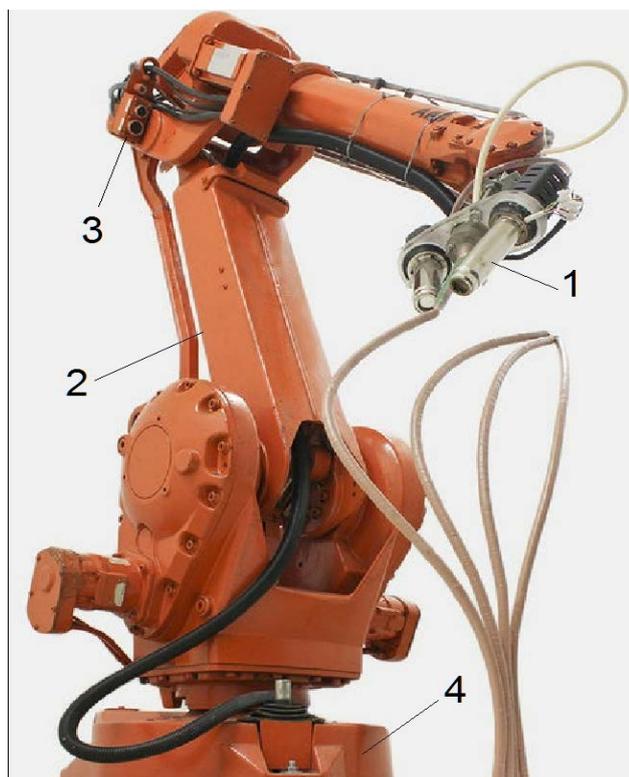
Схема 3D-принтера на базе робота-манипулятора: 1 - экструдер - печатающая головка; 2 - подвижный корпус; 3 - датчики для стабилизации в пространстве (гироскоп, дальномер); 4 - передвижное устройство.
